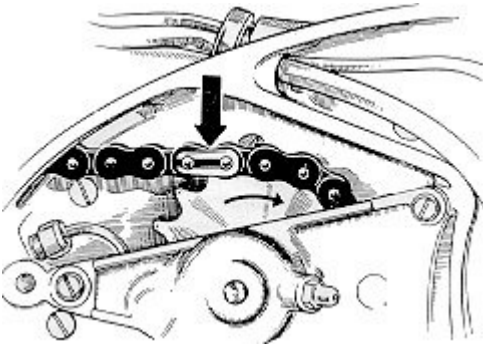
Kettenverschluß mit Schmiernippel für Tachoantrieb
